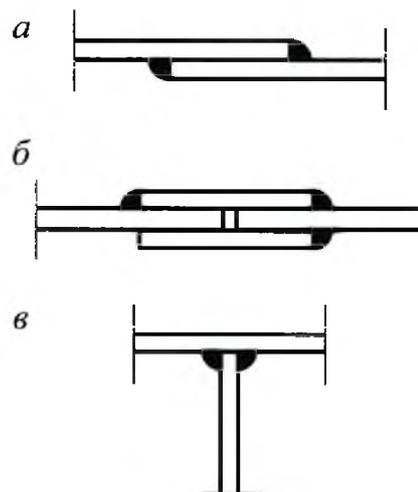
Сварные соединения: а — внахлестку; б — с накладками; в — в тавр
